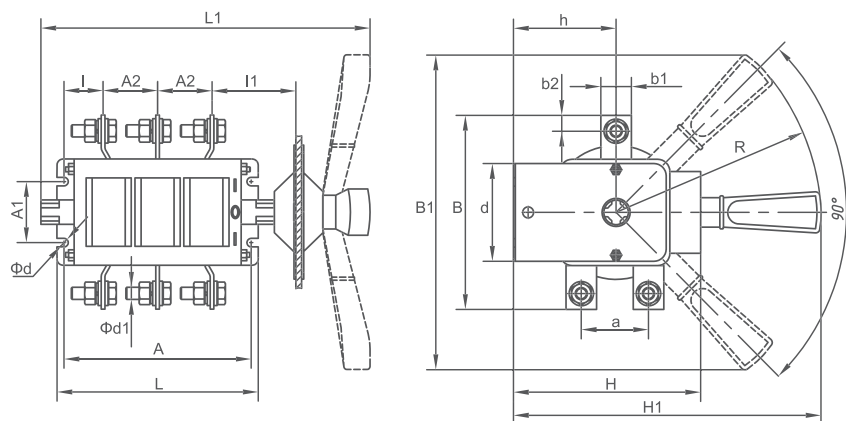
Выключатель-разъединитель универсальный трехполюсный на два направления с д/г камерами, съемная левая/правая рукоятка
